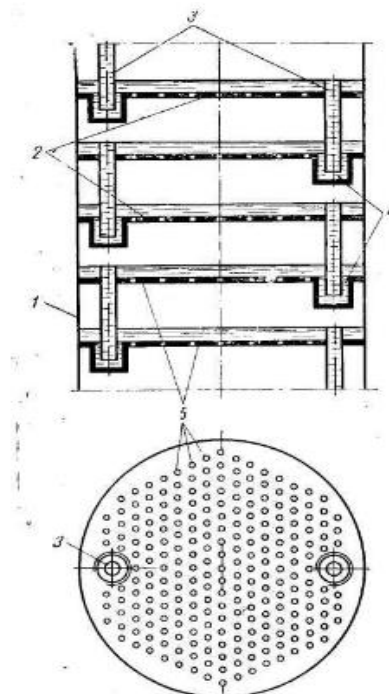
Схема устройства ситчатой тарелки: / — корпус колонны; 2 — тарелка; 3 — сливная труба; 4 — гидравлический затвор; 5 — отверстия.
